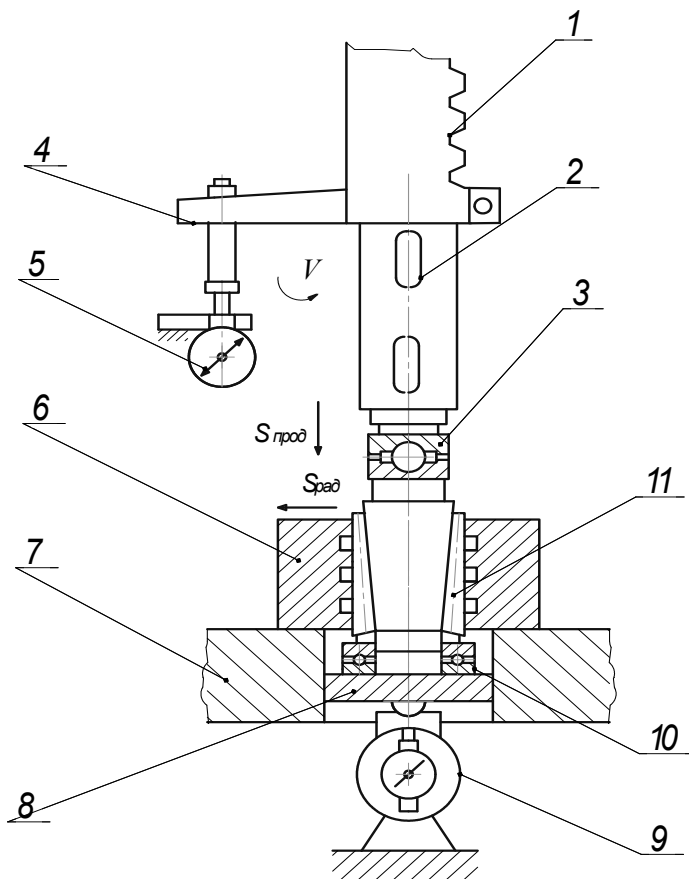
Схема дослідної установки для вимірювання зусилля обробки: 1 – піноль; 2 – шпиндель; 3 – шарнир; 4 – упор регульований; 5 – індикатор переміщення шпинделя; 6 – деталь; 7 – стіл; 8 – поршень; 9 – динамометр; 10 – підшипник упорний; 11 – ролик.
